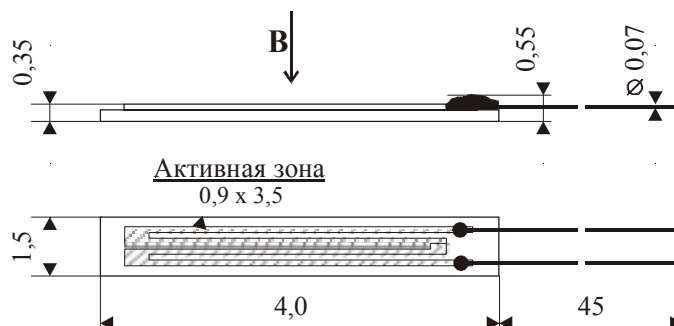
Внешний вид и габариты магниторезисторов СМ4-1
